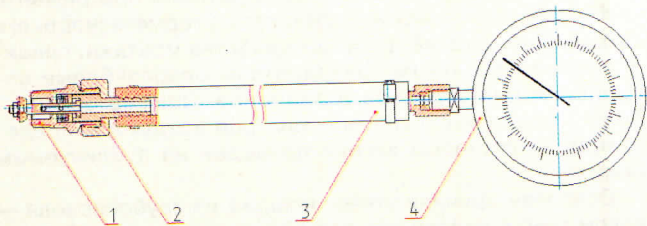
Приспособление для измерения давления воздуха в тормозном цилиндре:
